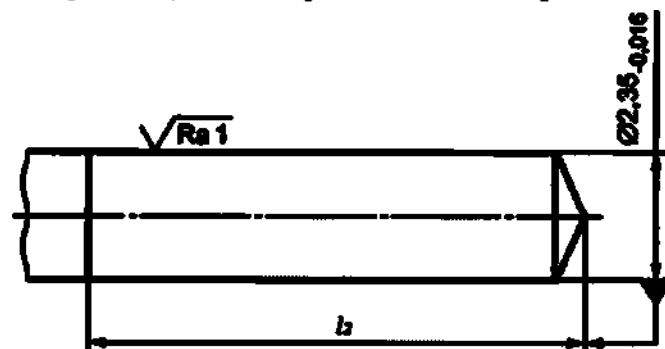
Размеры, допуски и шероховатость поверхности для хвостовика типа 2
